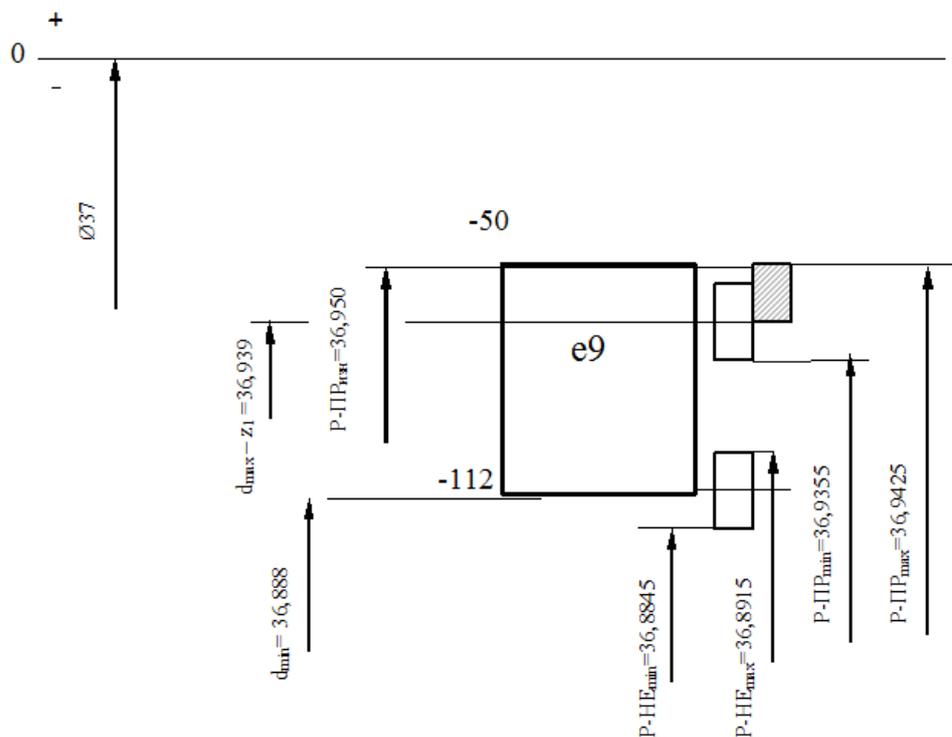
Схема полей допусков калибра-скобы для контроля вала 37e9
